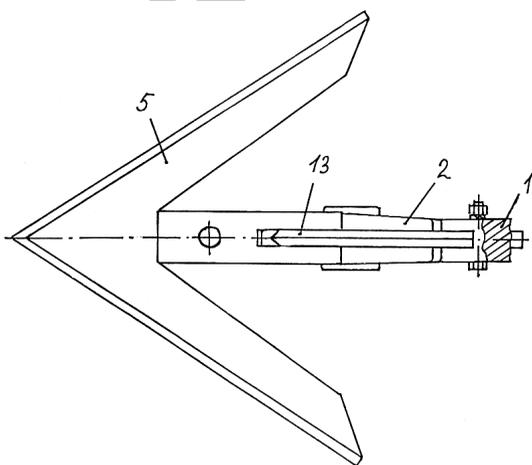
Рабочий орган культиватора (вид сверху)
